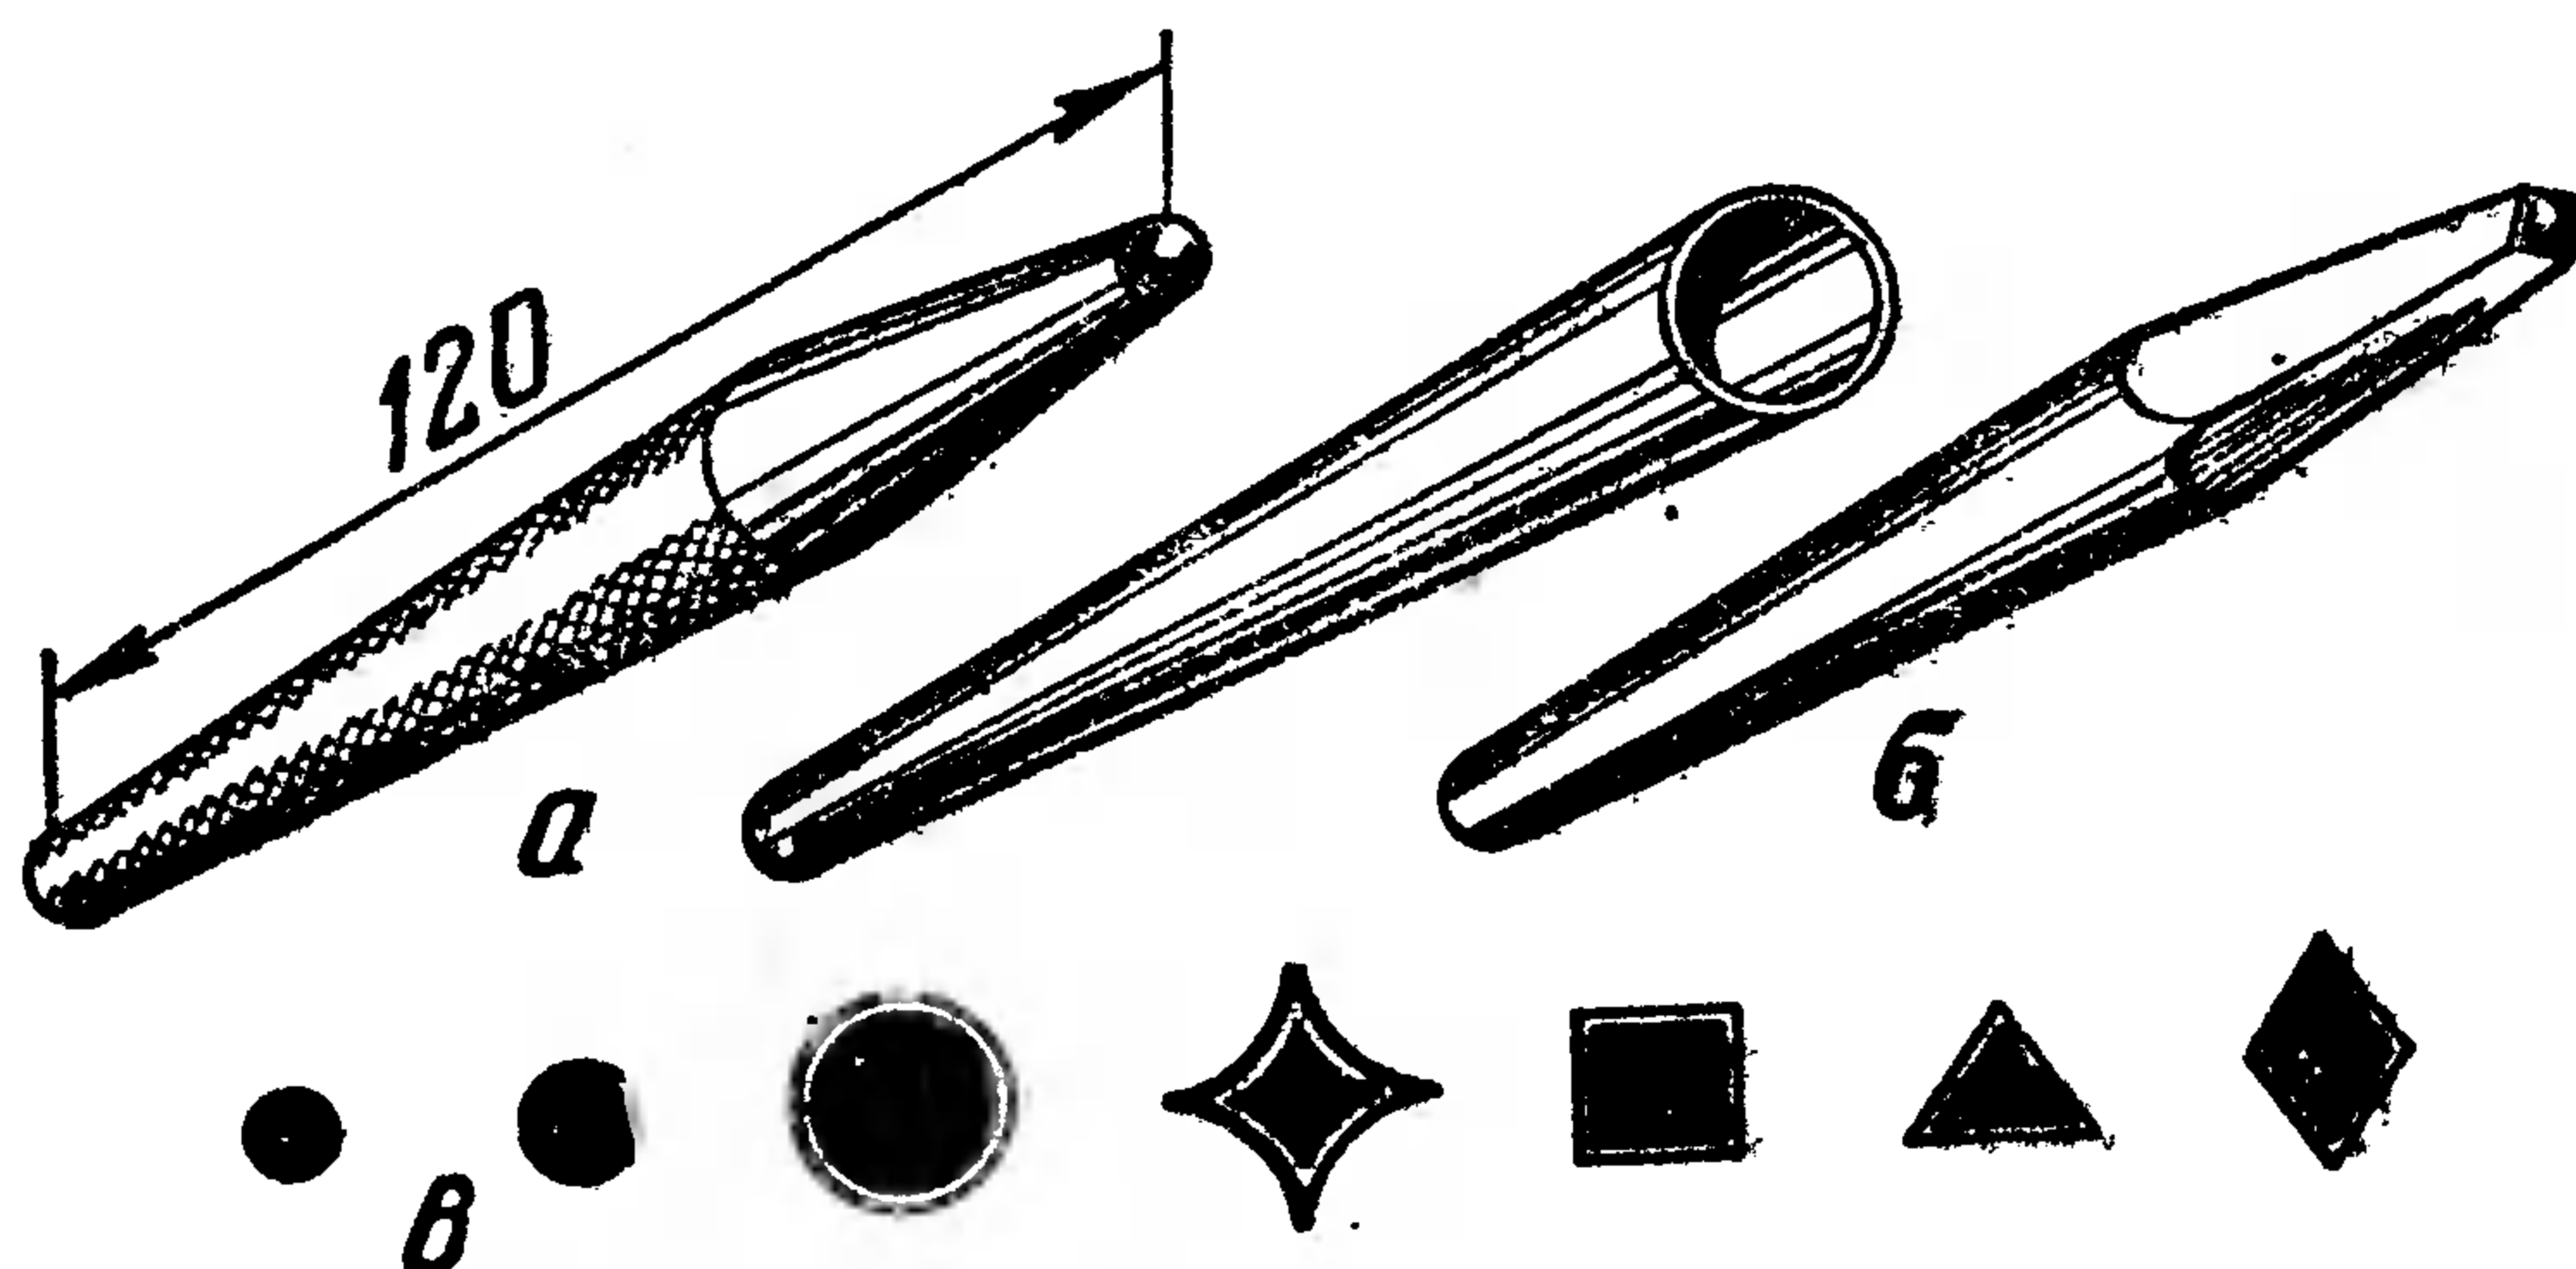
Инструменты для тиснения: а — стержни; б — трубочки; в — профиль рабочей части пуансонов и трубочек.
